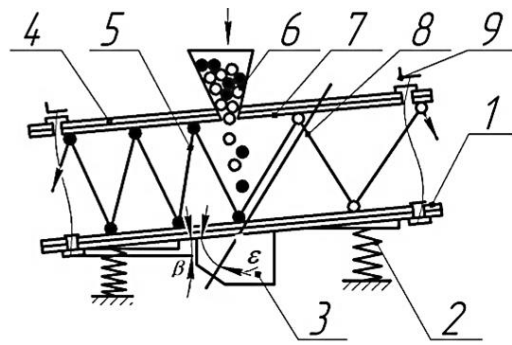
Схема сепаратора з відбивною робочою поверхнею:
